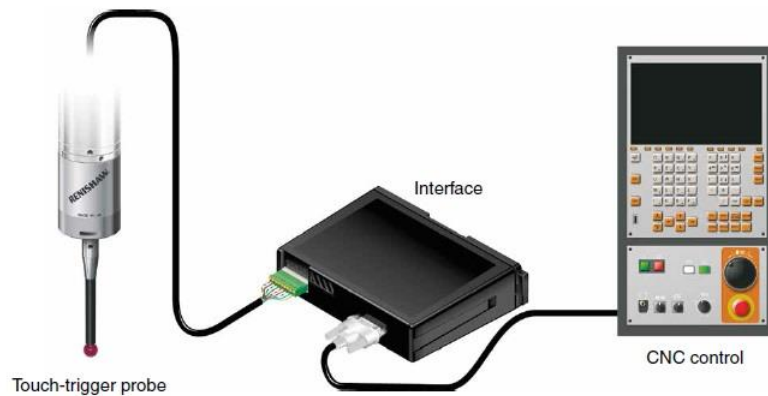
Transmissão de Informação por Cabo (Renishaw, Probing Systems for CNC Machine Tools, 2014)
